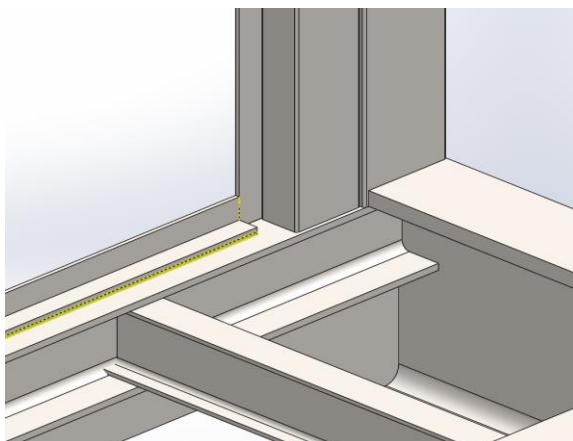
Colocación de porta-luces y perfil L exterior en cola.
